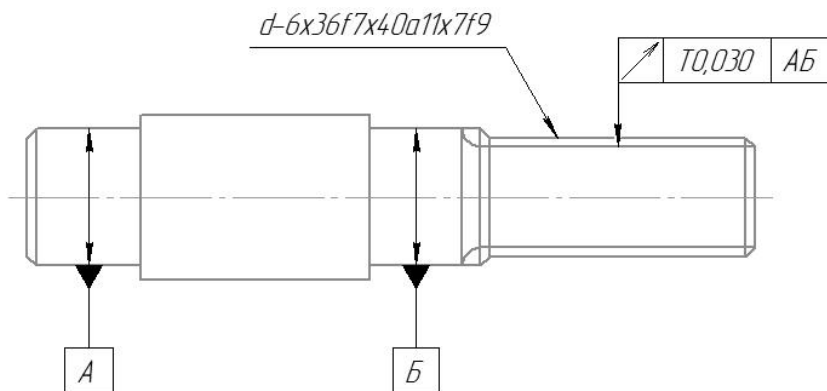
Обозначения допусков радиального биения элементов наружной шлицевой поверхности
